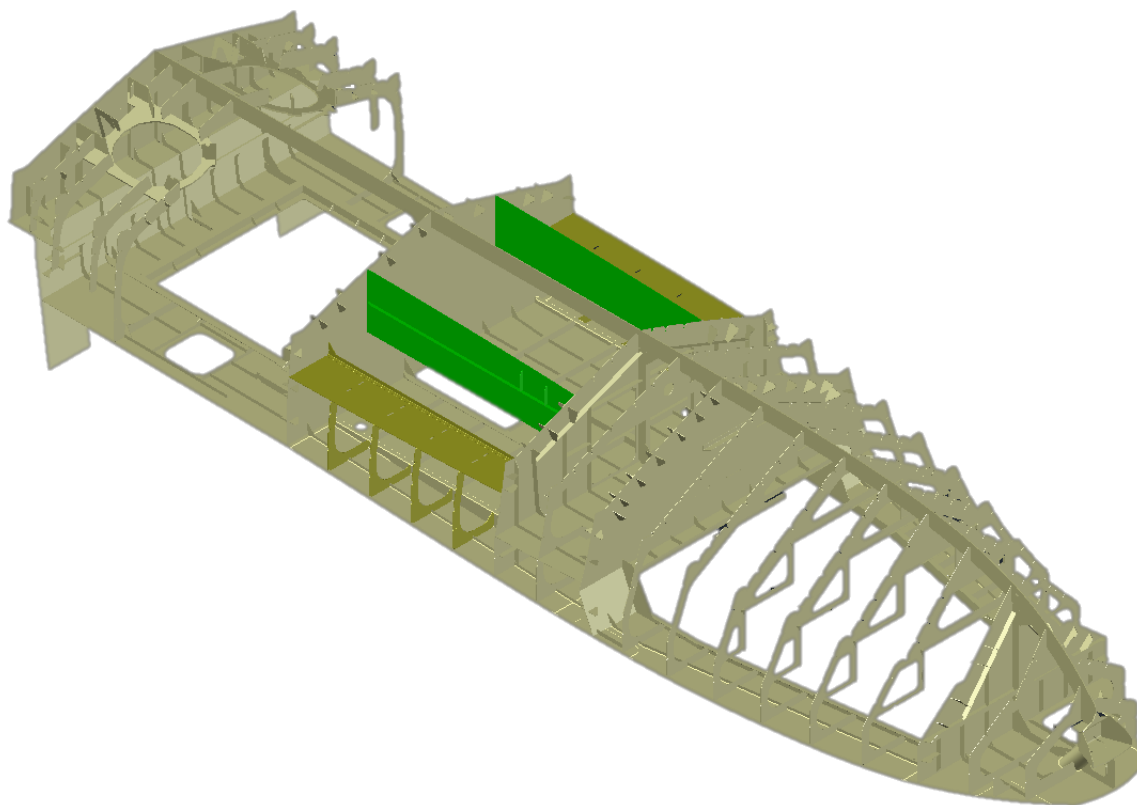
Montaža rebara sa temeljem propulzora
